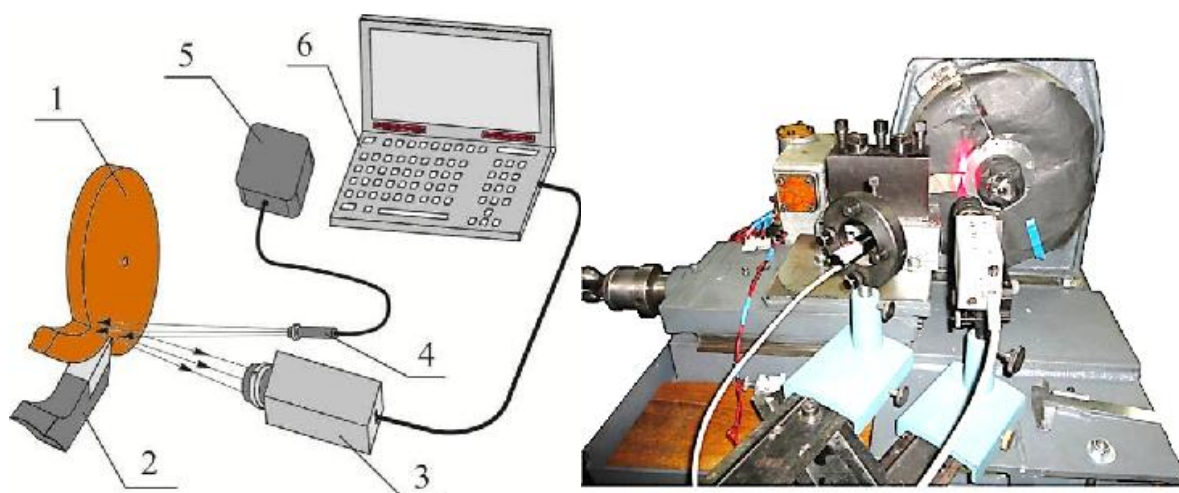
Лабораторно-экспериментальный стенд: 1 – диск (заготовка), 2 – резец с динамометром, 3 – цифровая видеокамера, 4 – лазер, 5 – блок питания лазера, 6 – персональный компьютер
